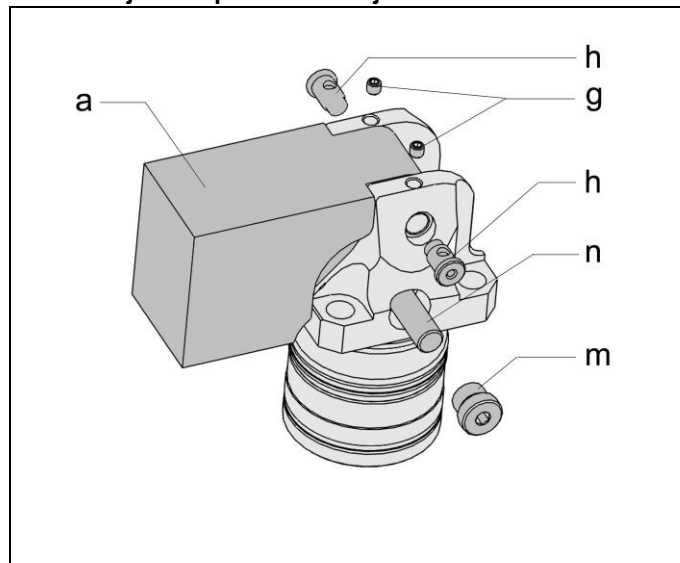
Desmontaje / montaje de la palanca de sujeción
